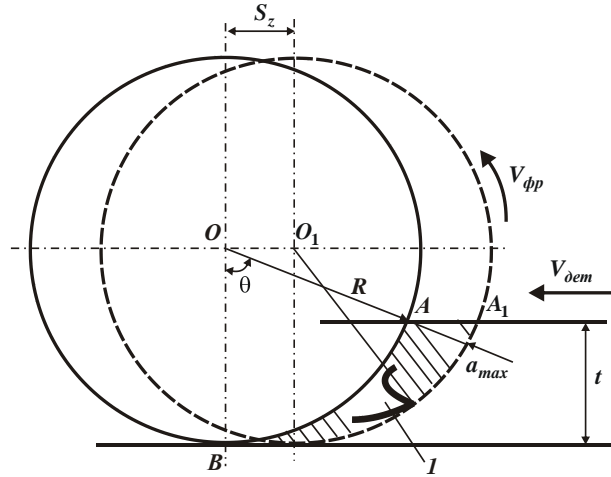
Расчетная схема параметров процесса фрезерования цилиндрической фрезой: 1 – зуб фрезы.
